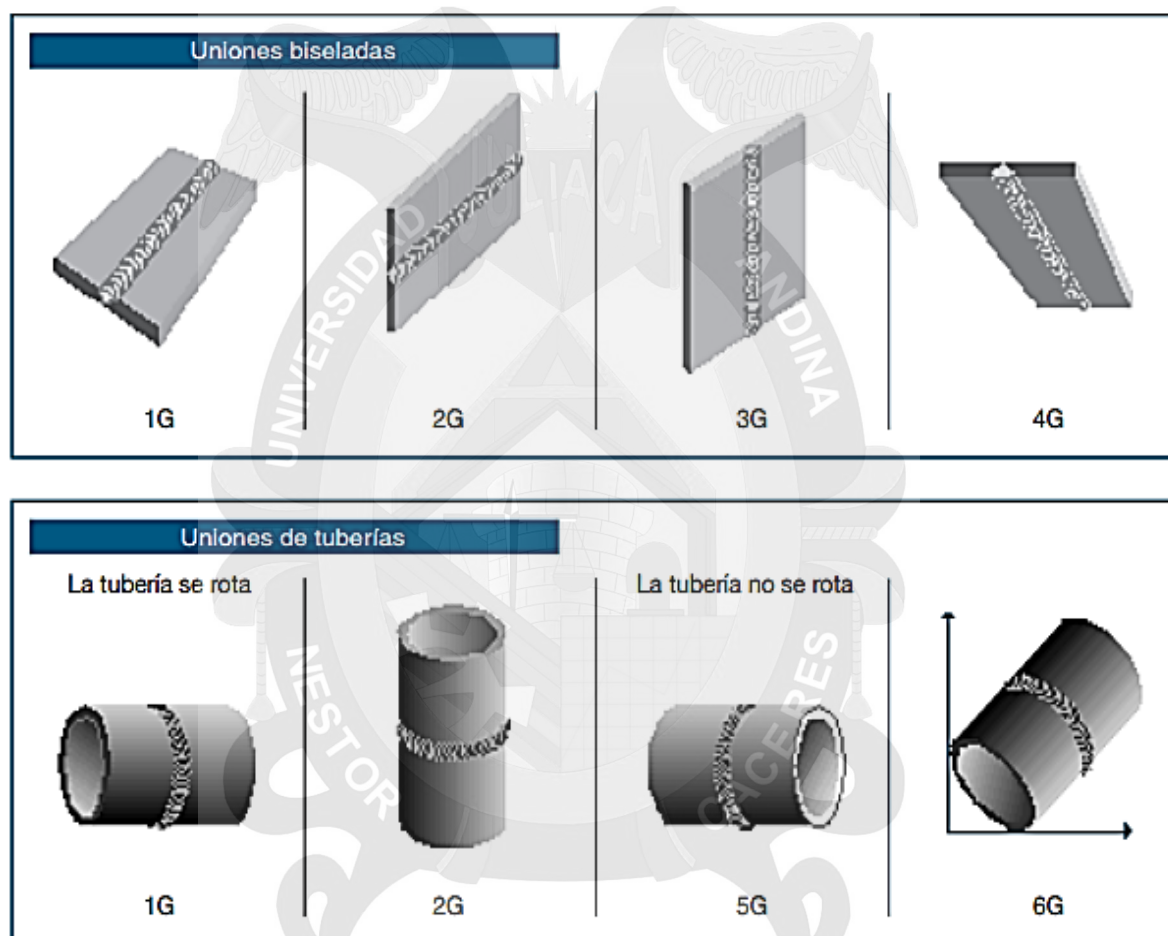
Código de posiciones de soldar para soldaduras de garganta utilizadas para cualificar operadores. Posiciones de las pruebas.
